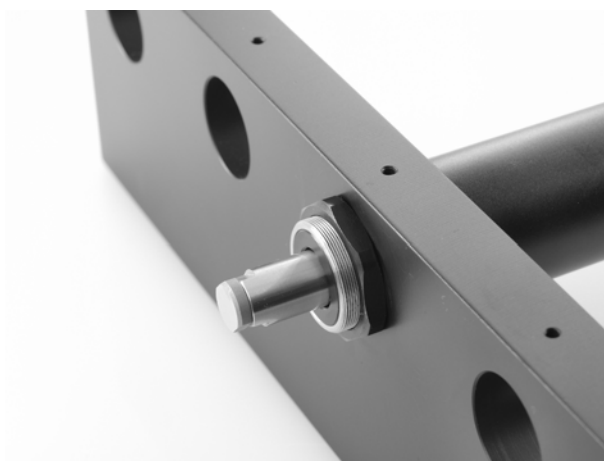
Beispiel für den Einbau eines Linearaktors (hier: ein M-235)
